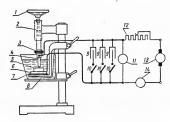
Станок для электроискрового изготовления полостей и отверстий в металле:
